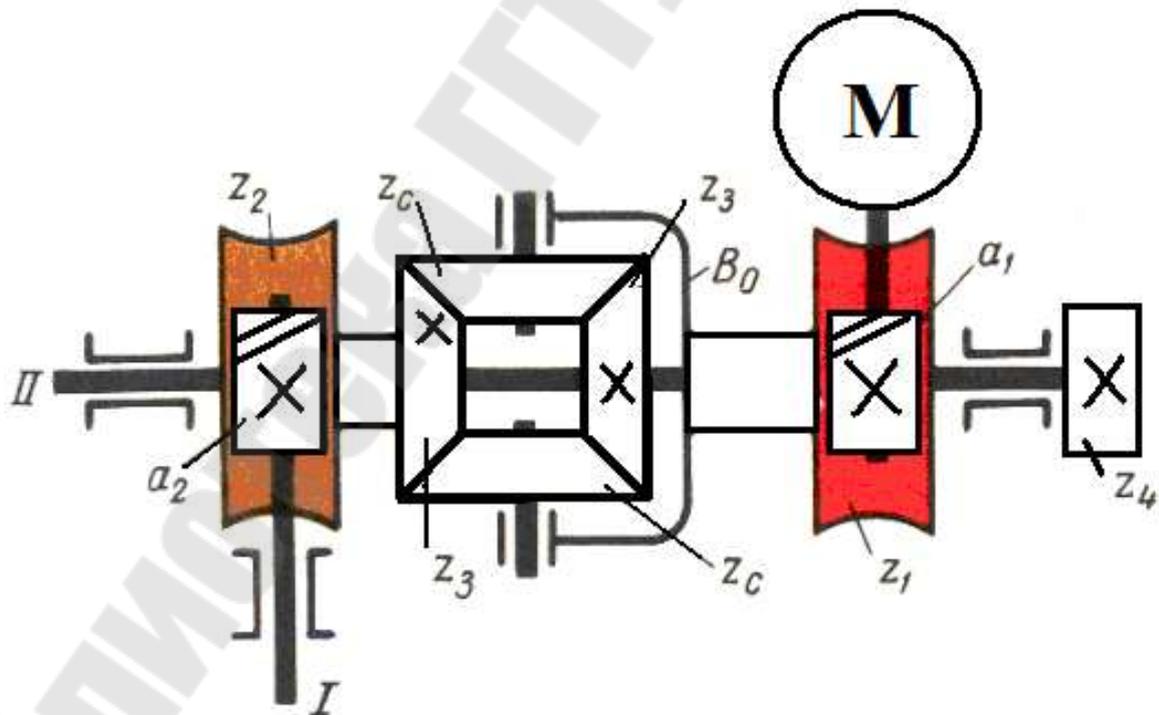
Схема планетарного механизма с коническими колёсами
